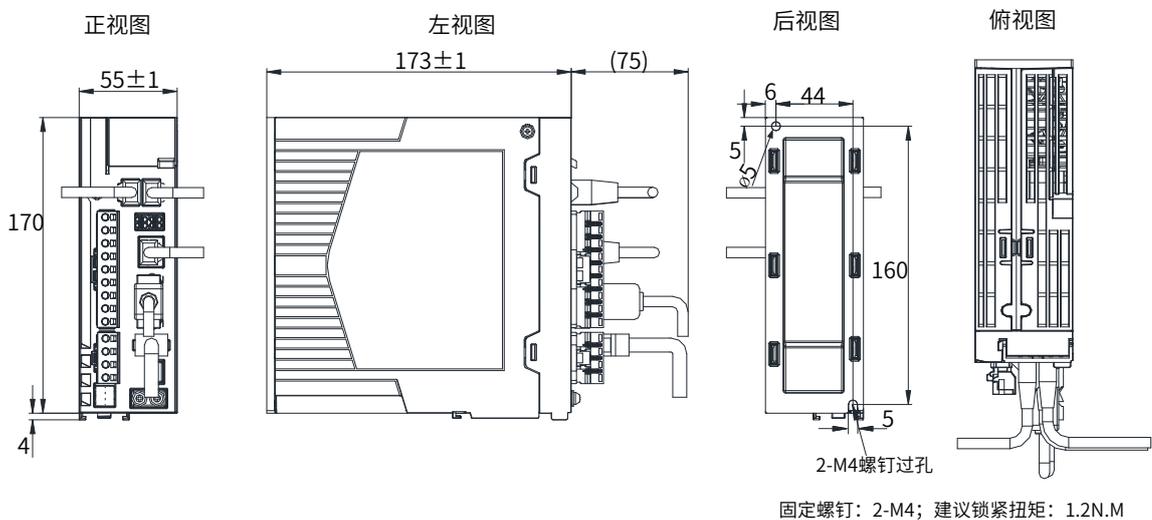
SIZEC 外形尺寸图 (单位: mm)
